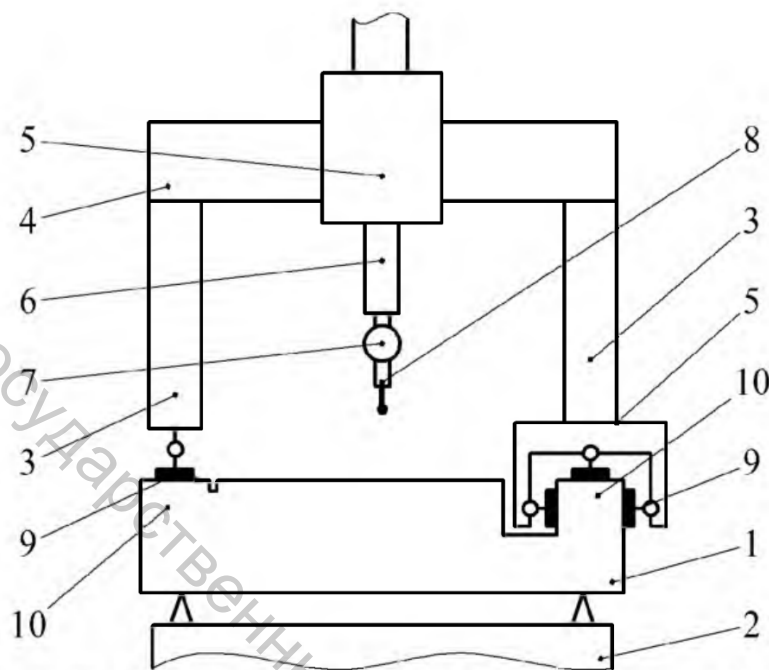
Принципиальная схема конструкции типовой КИМ портальной компоновки: 1 – стол; 2 – опорная рама; 3 – стойки; 4 – траверса; 5 – каретка; 6 – пиноль; 7 – поворотная головка; 8 – измерительная головка; 9 – аэростатические опоры (подшипники); 10 – направляющие (на рисунке – только ось X)
